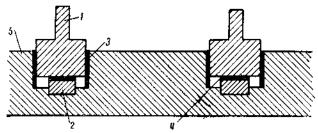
Приспособление из графитовой пластины для фиксации деталей при пайкс в печи вольфрамовых контактов для магнето автомобилей:
